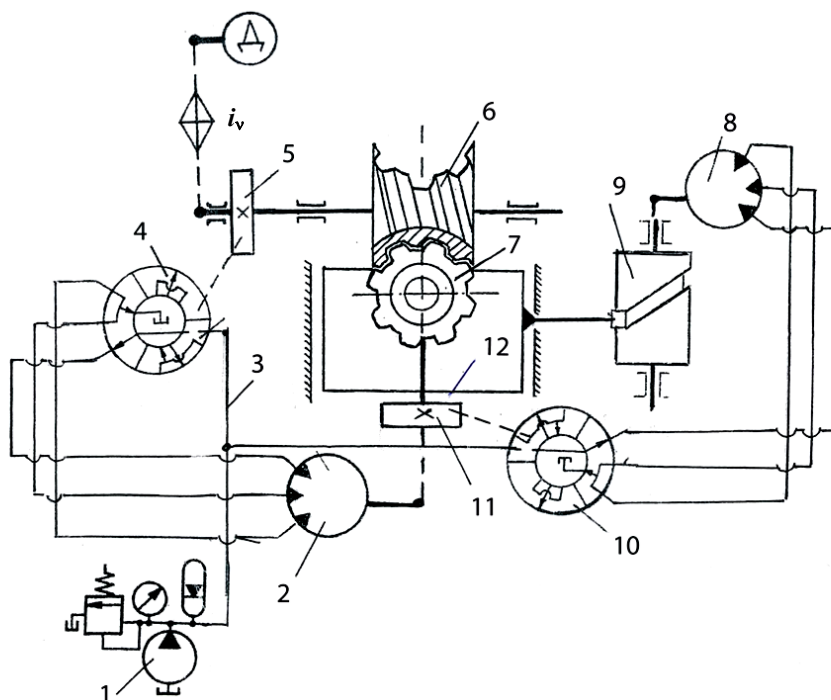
Структурная схема резьбонарезного станка с гидравлическими внутренними связями для нарезания глобоидных червяков обкаточным резцом
